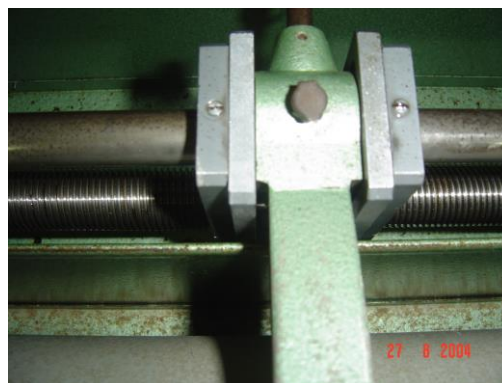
Máquina montada e detalhe de peça que foi completamente desmontada, limpa e lubrificada.
